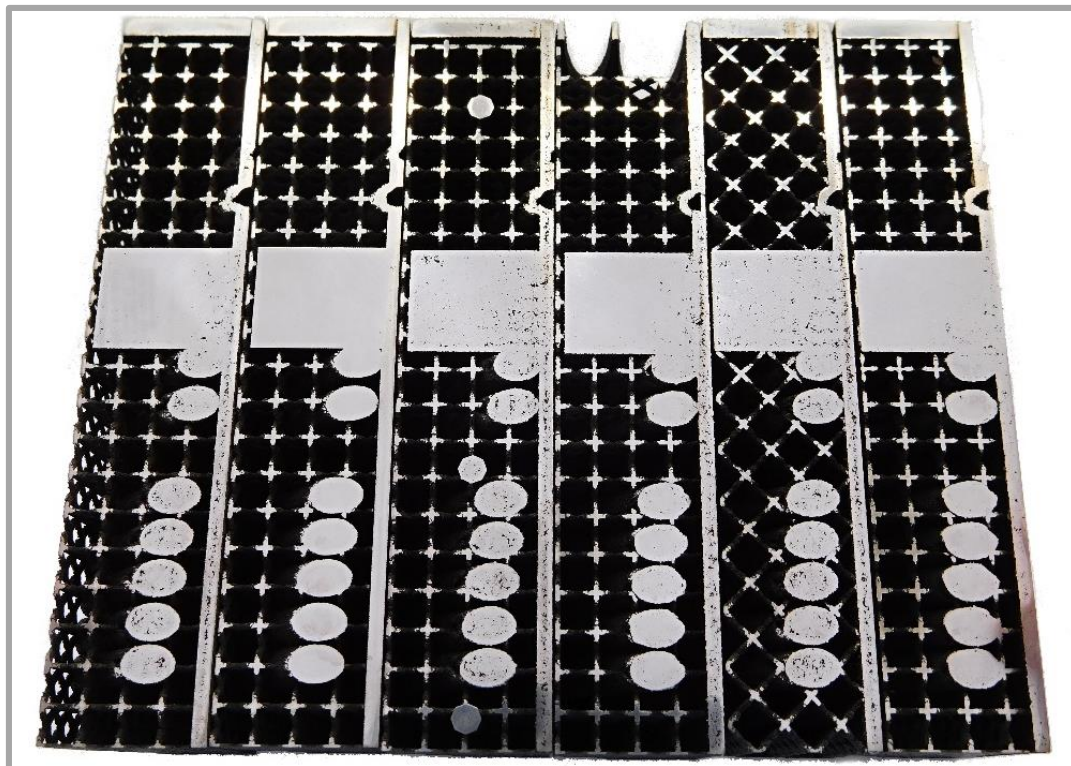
Optické srovnání skořepiny čtvrtiny segmentu odchylka 0,2 mm
